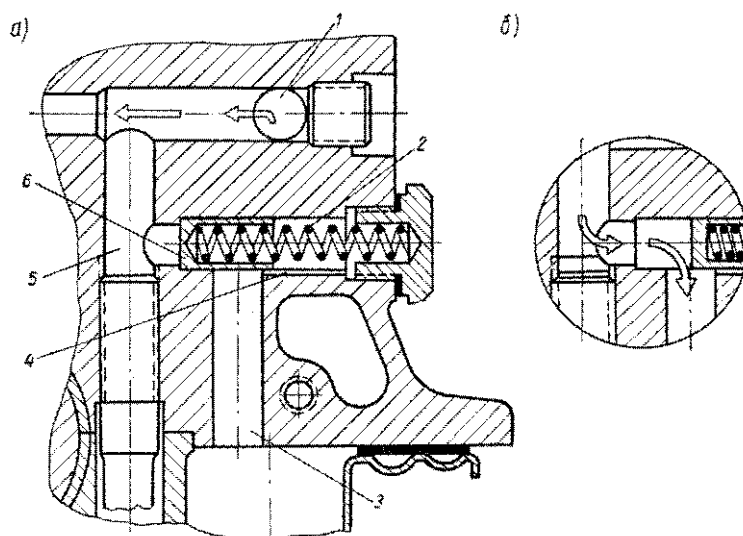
Схема подвода масла к редукционному клапану: а — редукционный клапан закрыт; б — редукционный клапан открыт;
